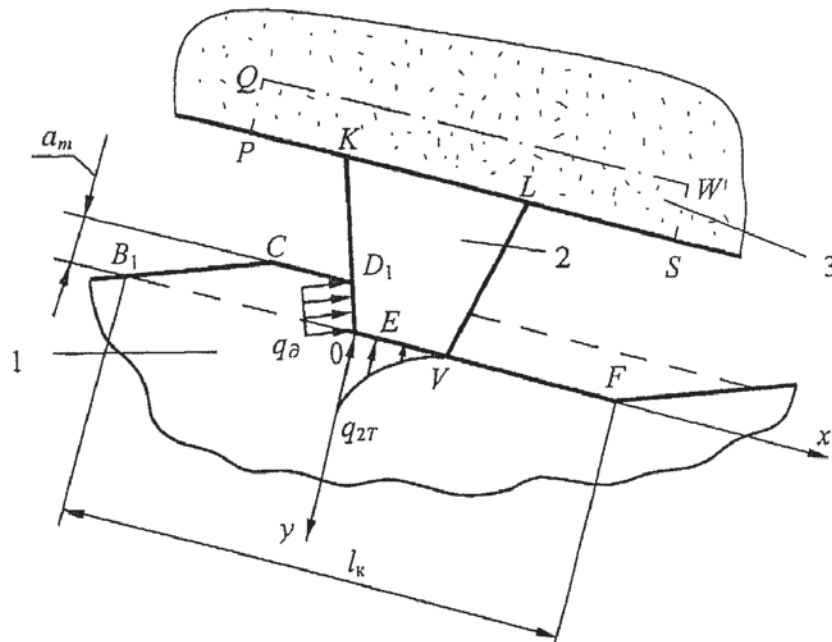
Схема контакта заготовки с пластически деформирующим а.з.: 1 — заготовка; 2 — а.з.; 3 — шлифовальный круг
